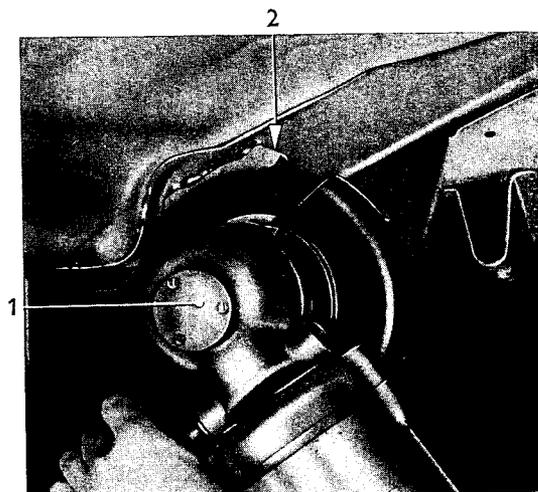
Flansch der inneren Hinterfederstütze am Hinterlängsträger abschleifen
